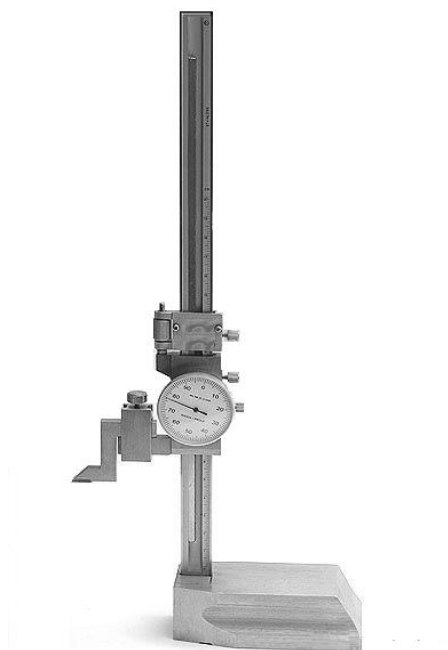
Общий вид штангенрейсмаса ШРК
